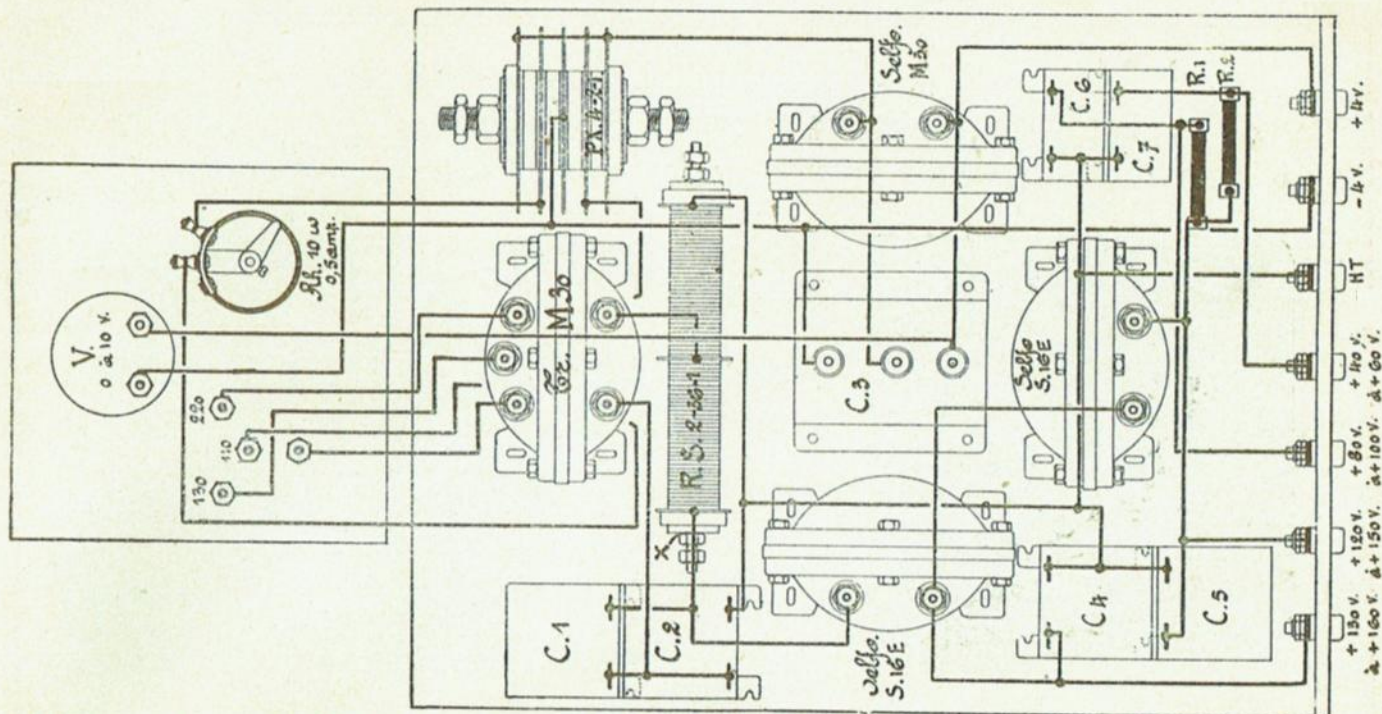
DETAIL DES PIECES NECESSAIRES AU MONTAGE
